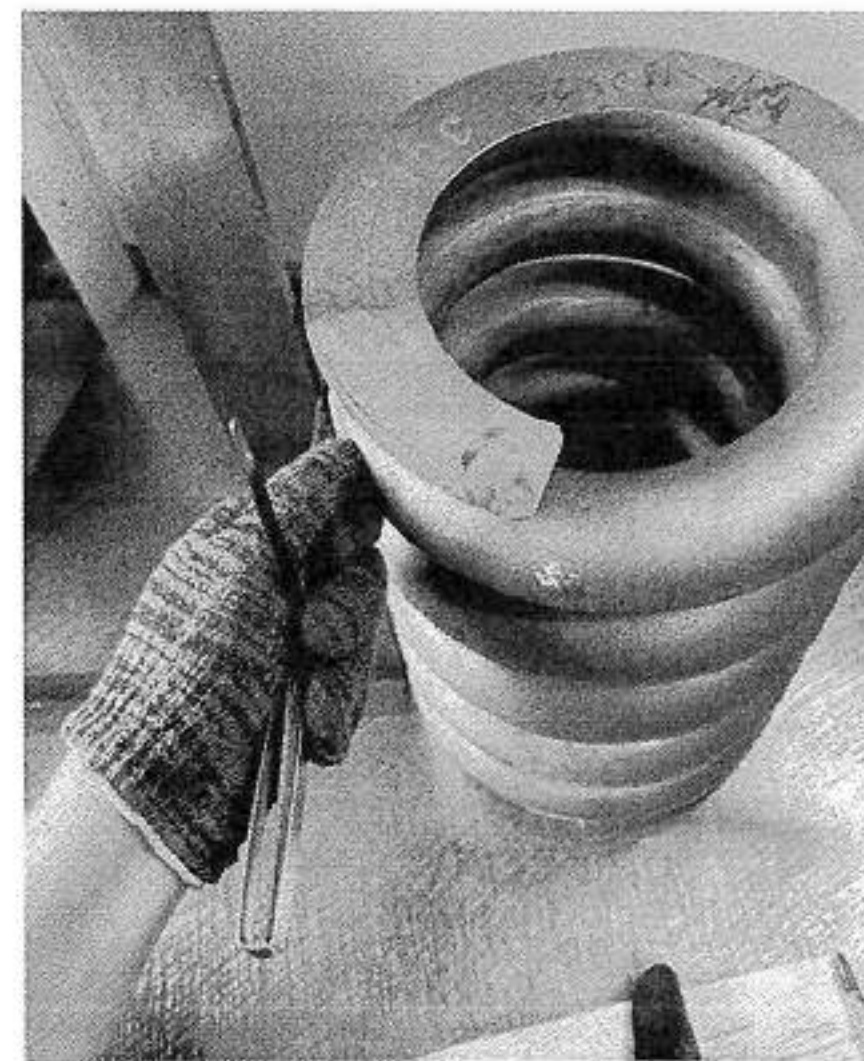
Проведение измерений допуска перпендикулярности оси пружины на поверочной плите поверочной и разметочной, тип № 1-2-1000×630
